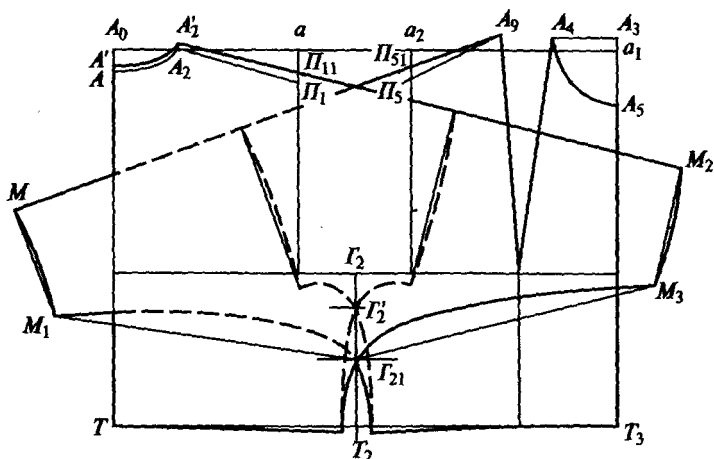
Чертеж конструкции изделия с цельнокроеными рукавами мягкой формы
